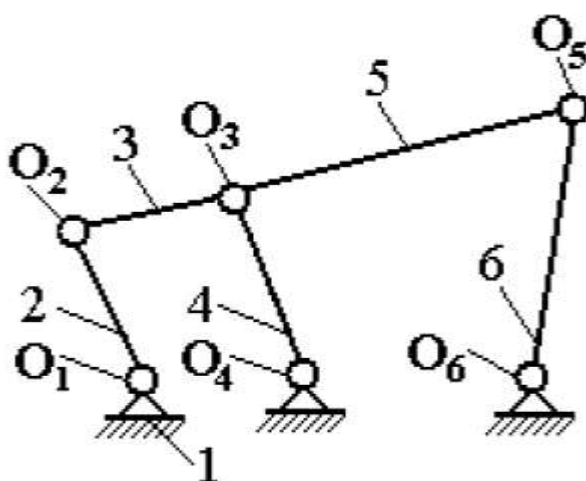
Шарнирно - рычажный шестизвенный механизм [100]
